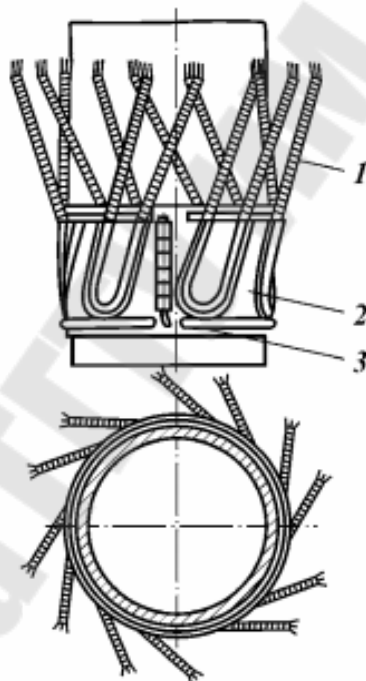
Скребок корончатый разъемный типа СК: 1 – рабочие элементы; 2- корпус; 3- штырь соединительный
